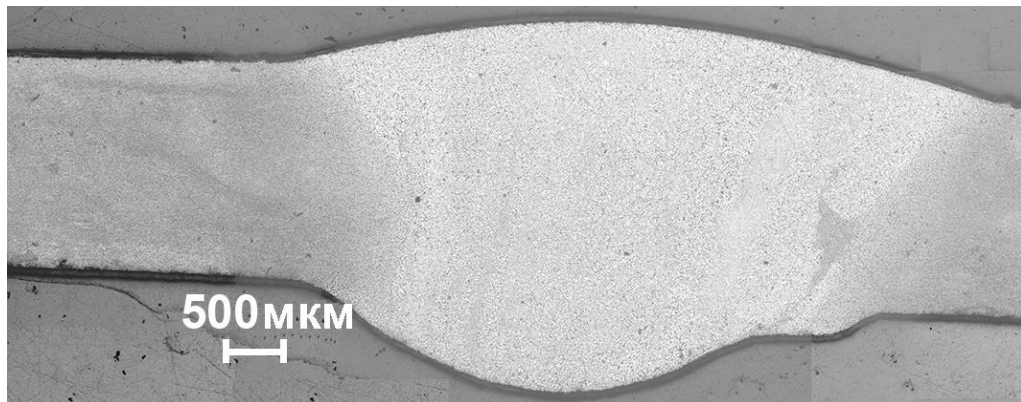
Изображение поперечного сечения сварного соединения алюминиевого сплава
